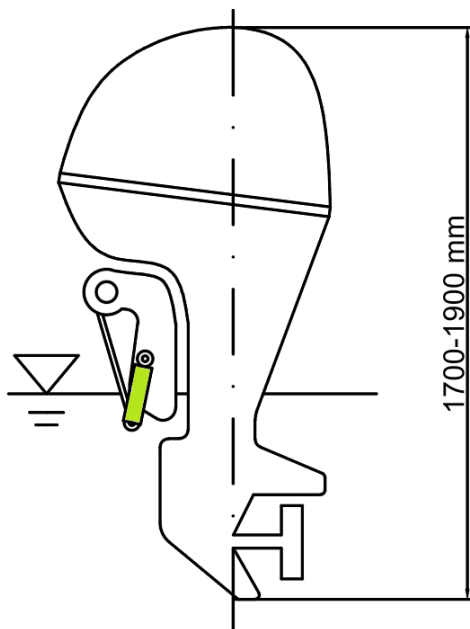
Power trim & tilt systém pro značku Honda [9]
